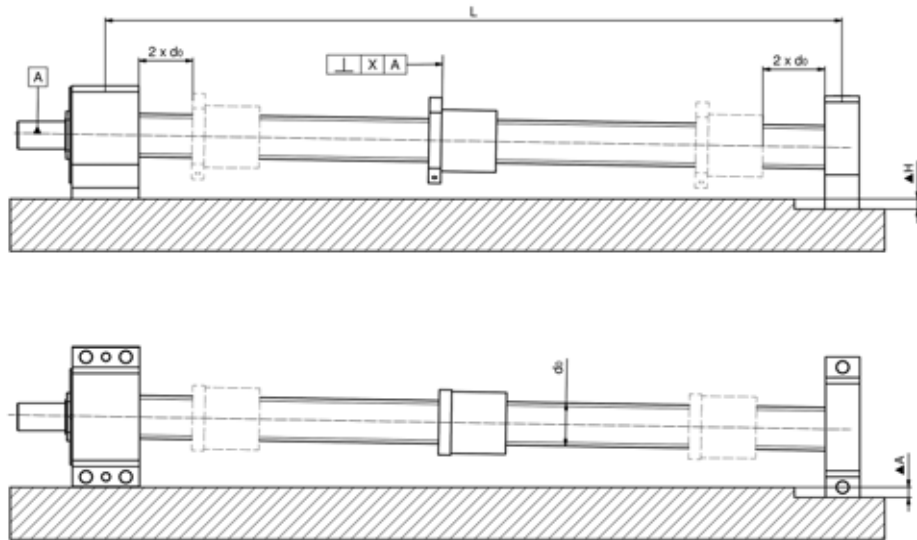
Definition der Montagetoleranzen von Kugelgewindetriebs
